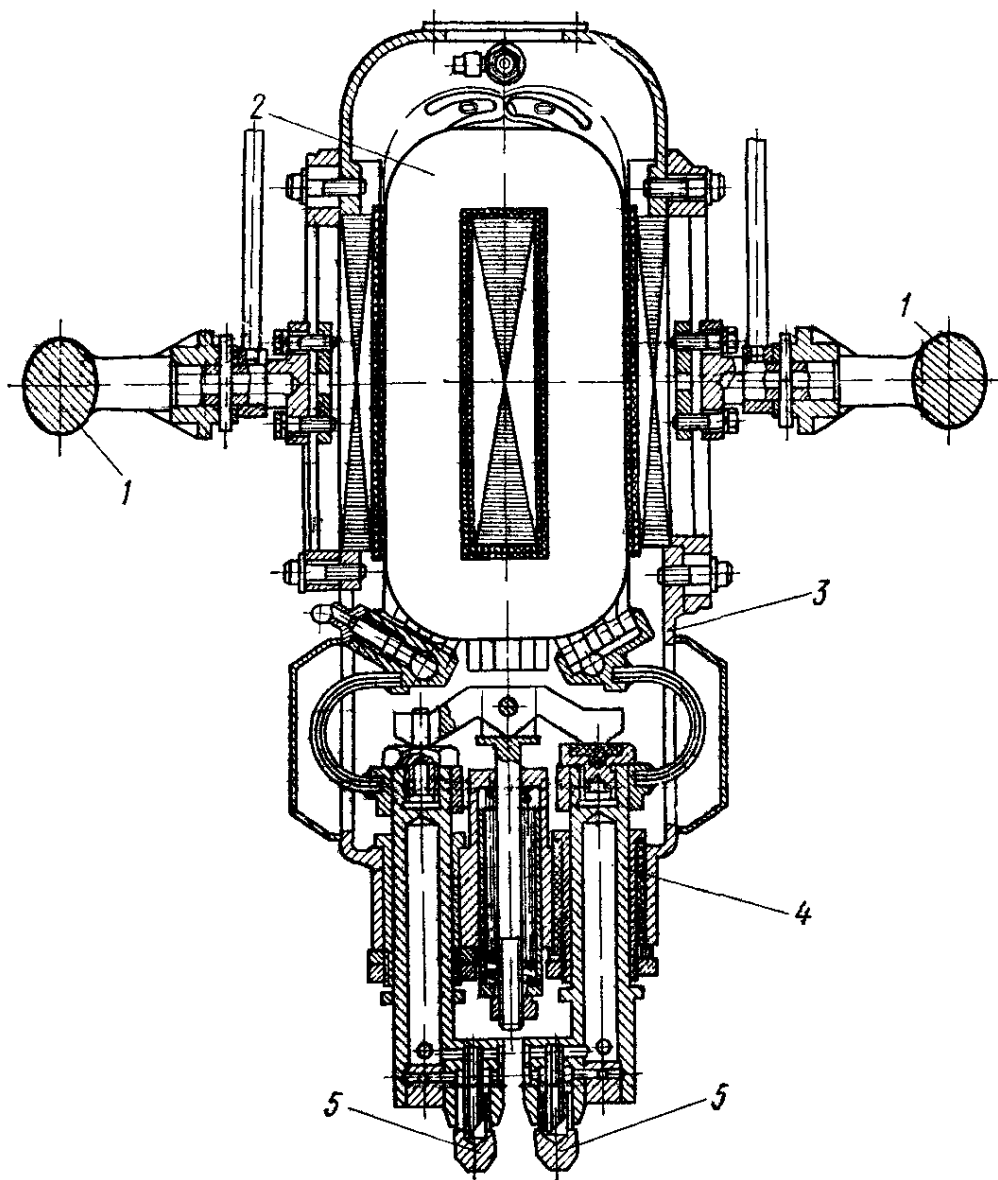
Пистолет К-264 для односторонней сварки:
